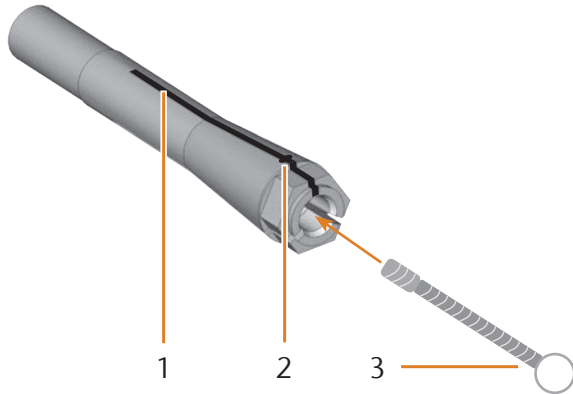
PULIZIA DELLA PINZA DI SERRAGGIO
